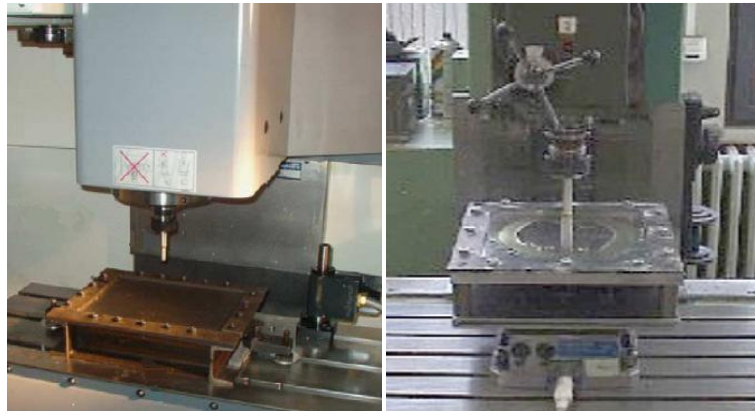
Máquinas-ferramenta adaptadas à estampagem incremental: centro de maquinagem (esq.) [AMB2005], e fresadora de bancada (dir.) [DUF2005].
